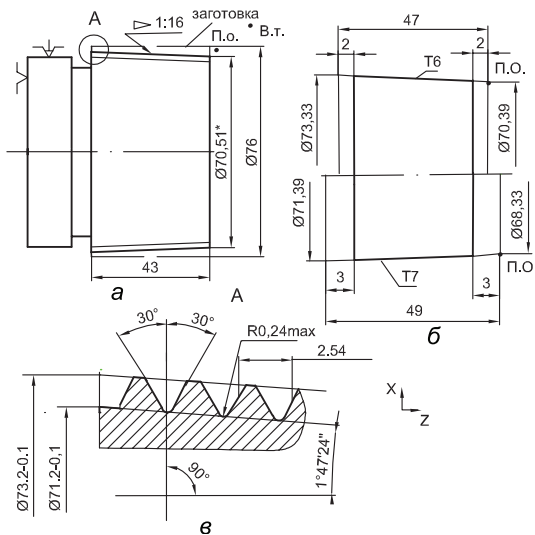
Нарізання зовнішньої різьби на деталі
